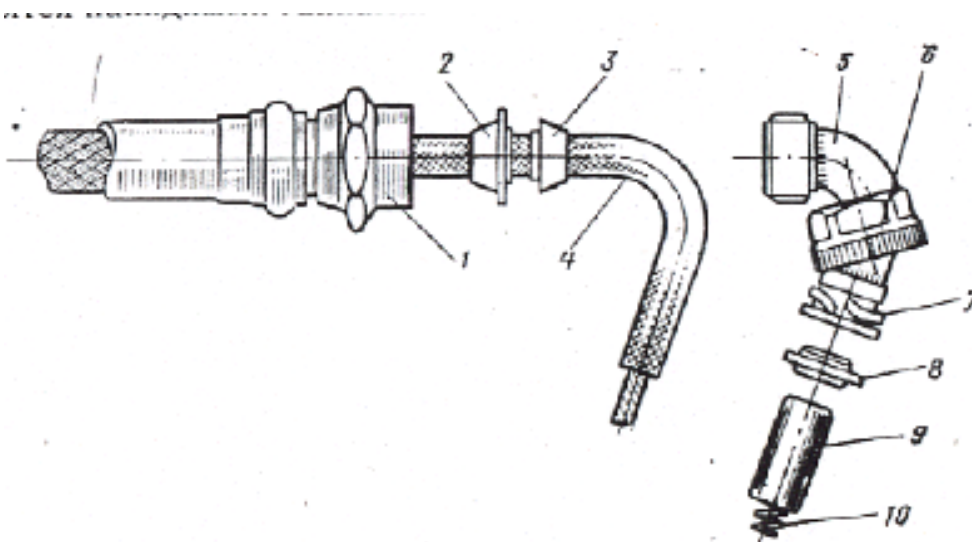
Соединение экранирующего шланга отъёмного проводника с угольником свечи, и угольника – со свечей:
